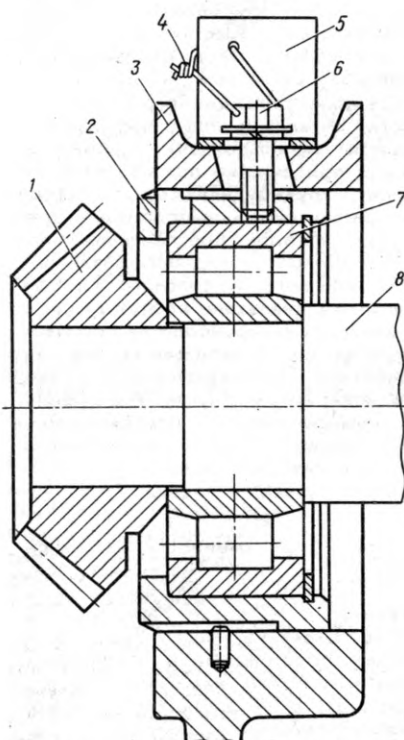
Установка роликового подшипника 70-32610 в редукторе: 1 — коническая шестерня; 2 — гнездо подшипника; 3 — картер редуктора; 4 — проволока диаметром 1,6 мм и длиной 100 мм; 5 — уголок; 6 — болт с шайбами 865Г ГОСТ 6402-70 и 10,02 ГОСТ 11371-78; 7 — подшипник; 8 — вал привода вентилятора охлаждения двигателей
